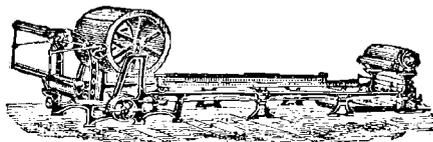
Machine à ramer avec pinces. système Tulpin.
